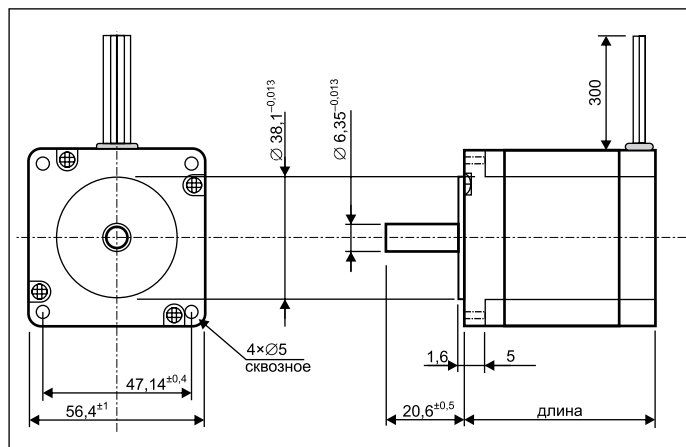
Габаритный чертеж шагового двигателя серии MT23FK
